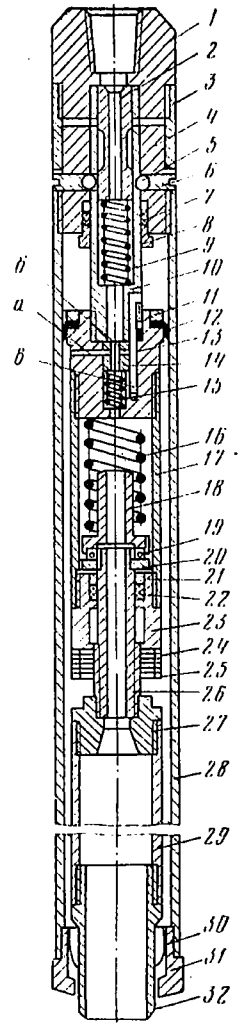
Двойной колонковый снаряд ДКС-10-89 конструкции А. А. Гребенюка.
